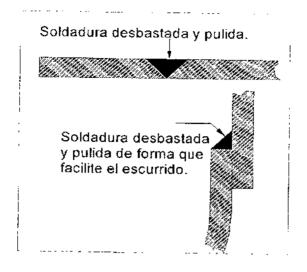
Soldaduras de láminas paralelas y láminas superpuestas
